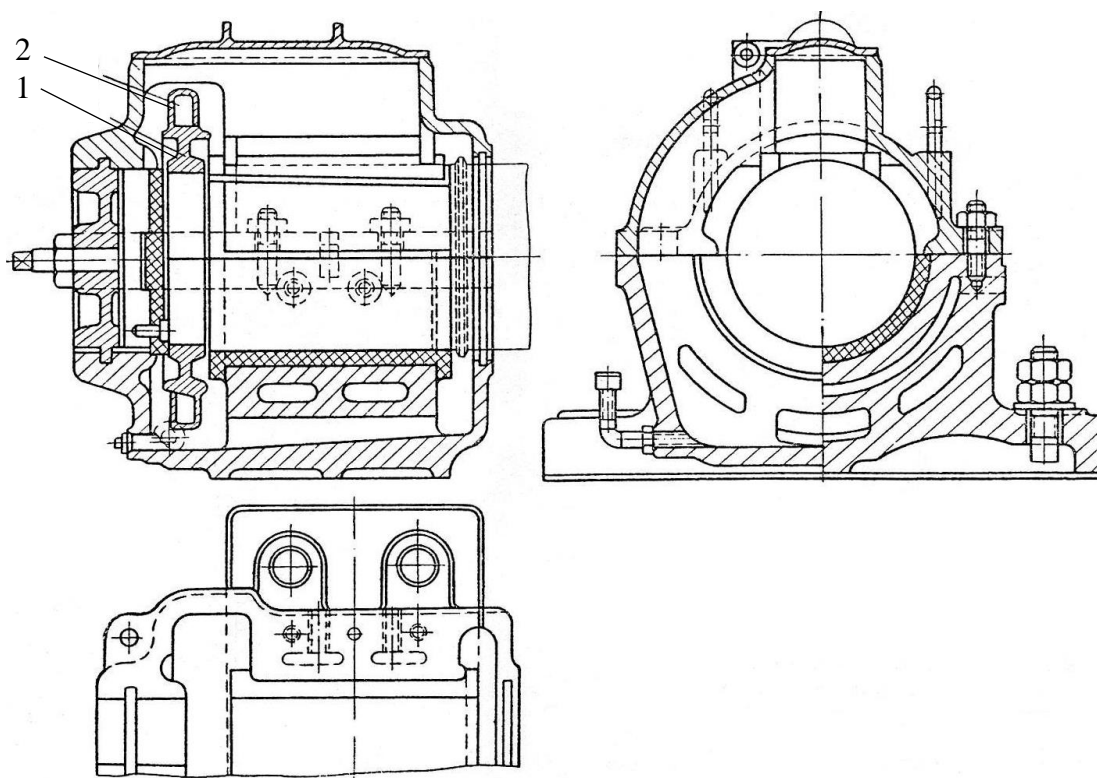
Опорный ролик на подшипниках скольжения:
